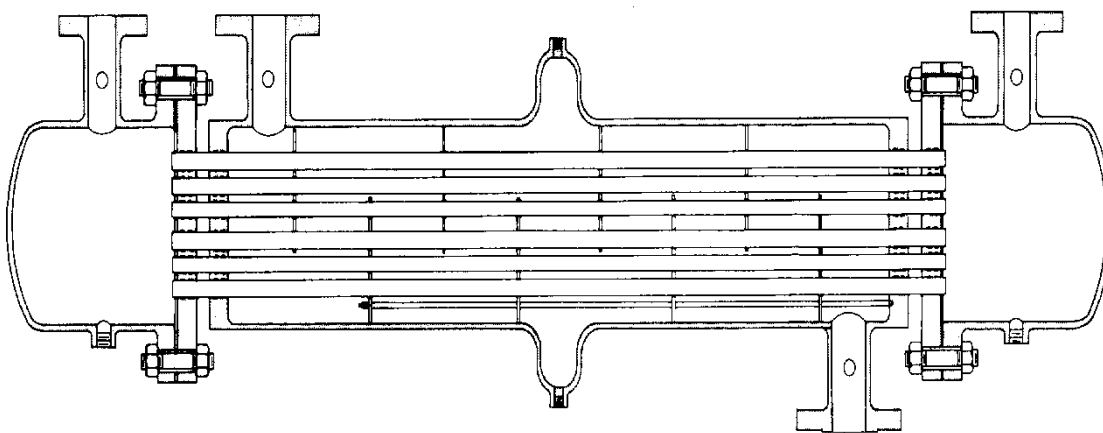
Usmernenie tekutiny v medzirúrkovom priestore pomocou prepážok [9]
